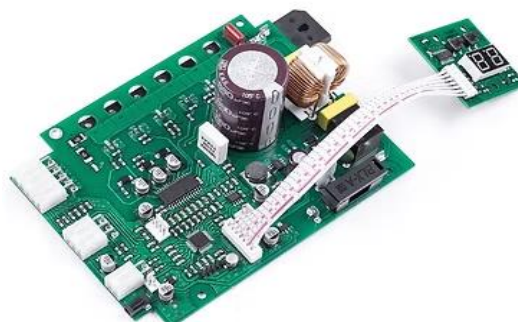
Pilote de moteur BLDC pour machine à coudre [21].
